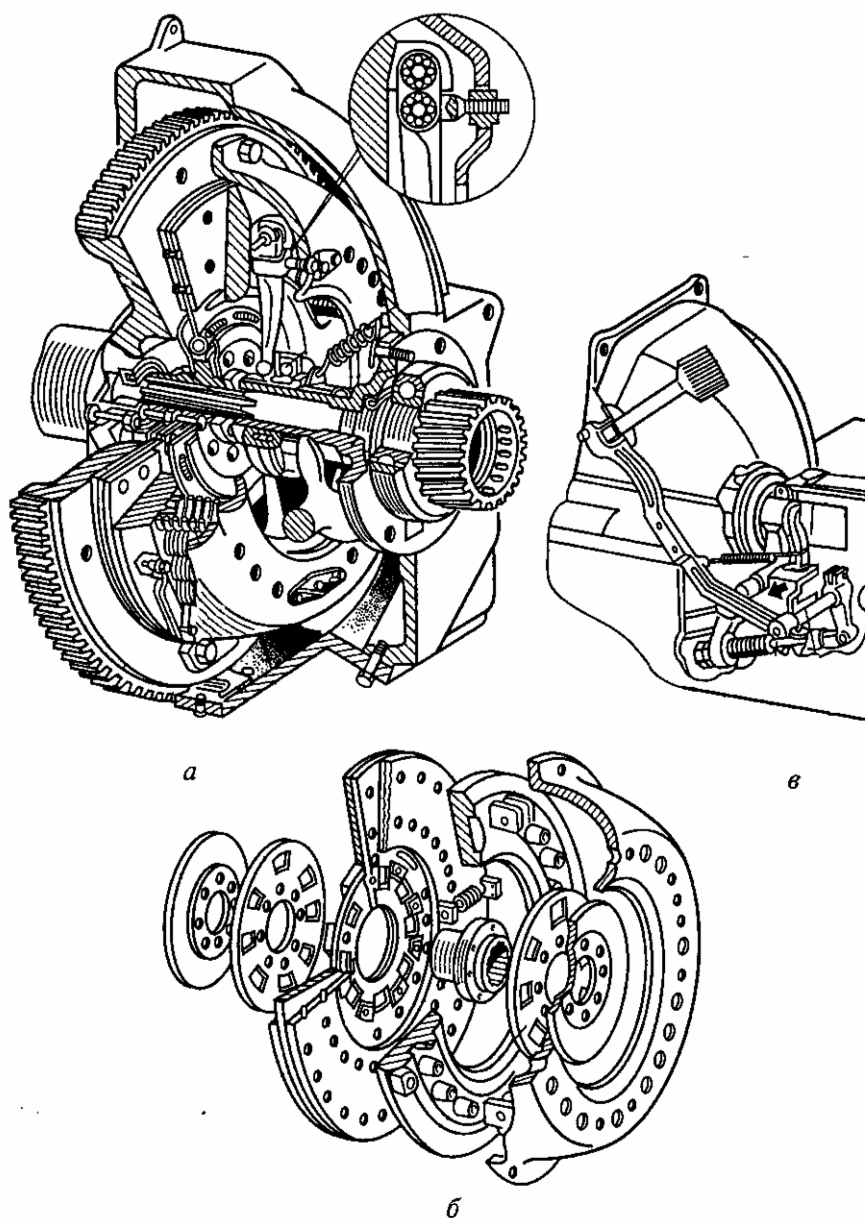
Сцепление (а), детали (б) и привод (в) сцепления грузовых автомобилей ЗИЛ
